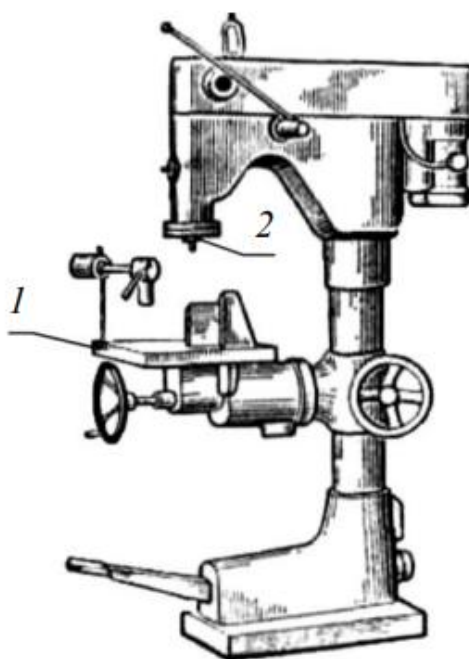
Загальний вигляд свердлильного одношпindelного верстата
